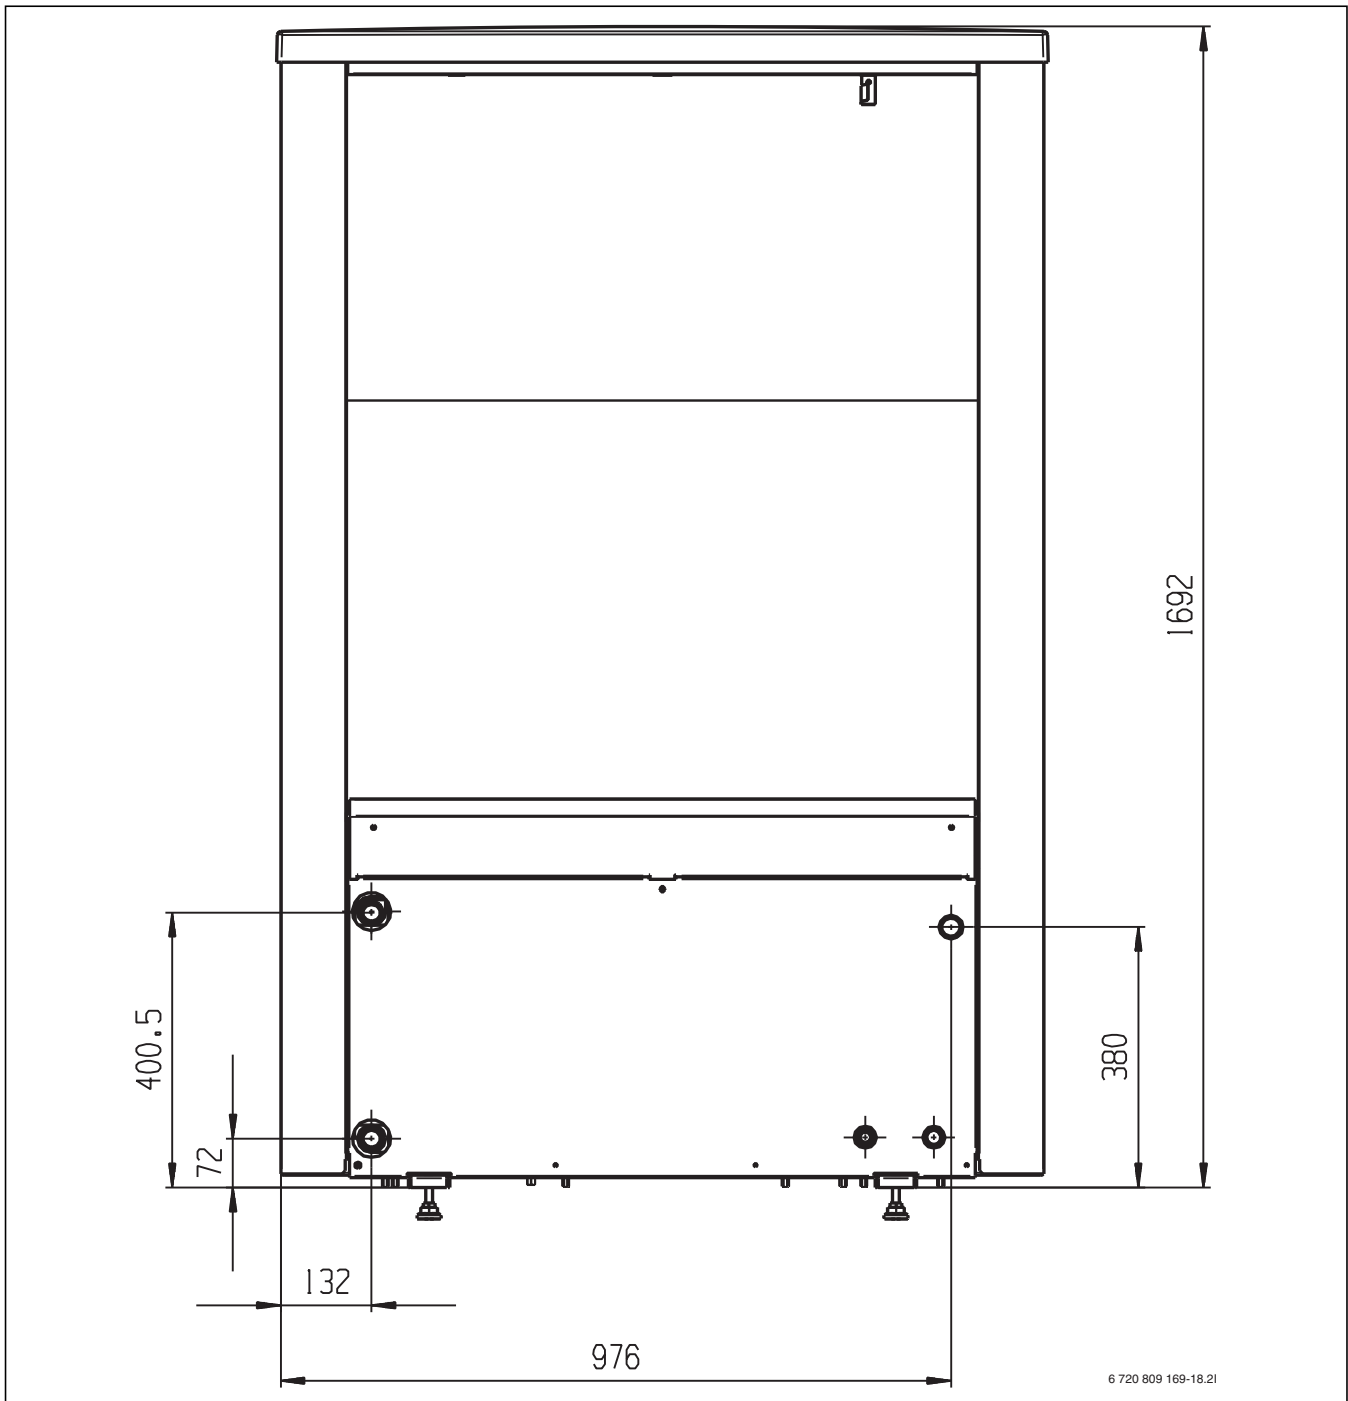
Dimensioni e attacchi del modello di pompa di calore AW 13-17, lato posteriore
